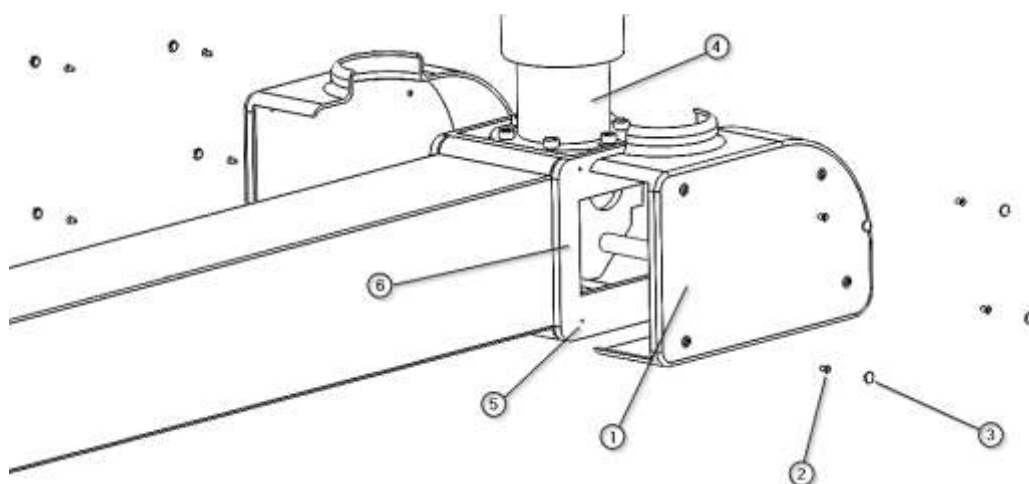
Montarea/demontarea capacelor de protecție pe tubul de tavan al unui braț motor
